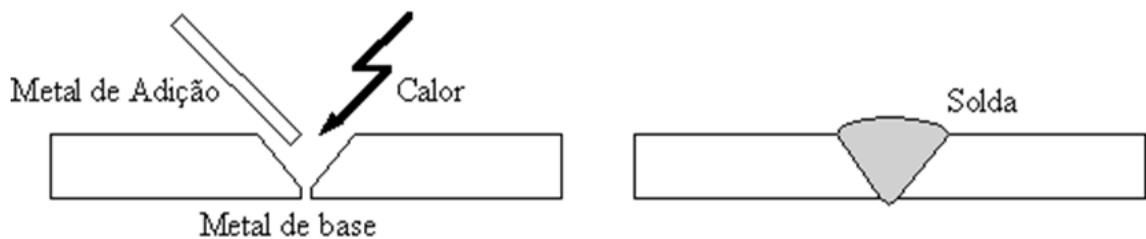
Modelo de soldagem por fusão <sup>(5)</sup>.
